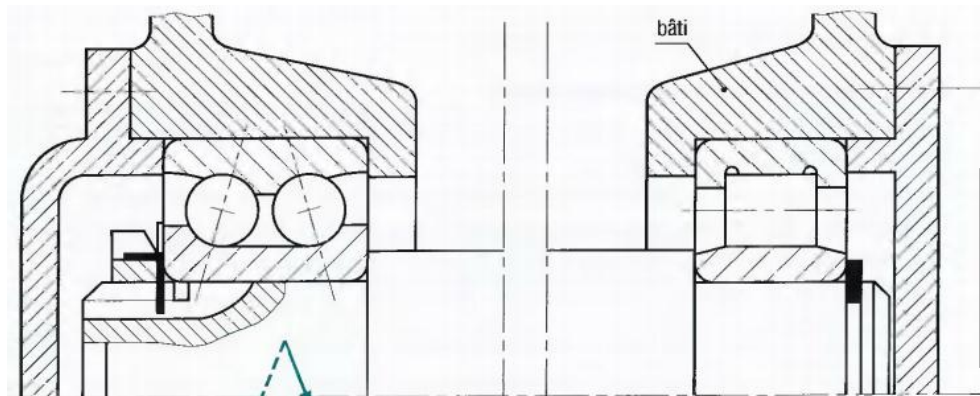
Exemple de montage Pour roulements de types BE et RU
